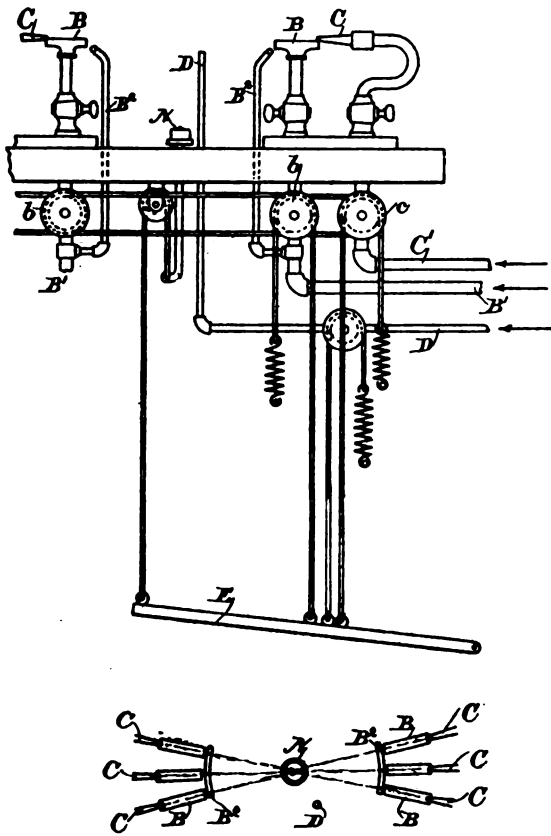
et 2. — Soufflage du verre Burnett et Doanc.
